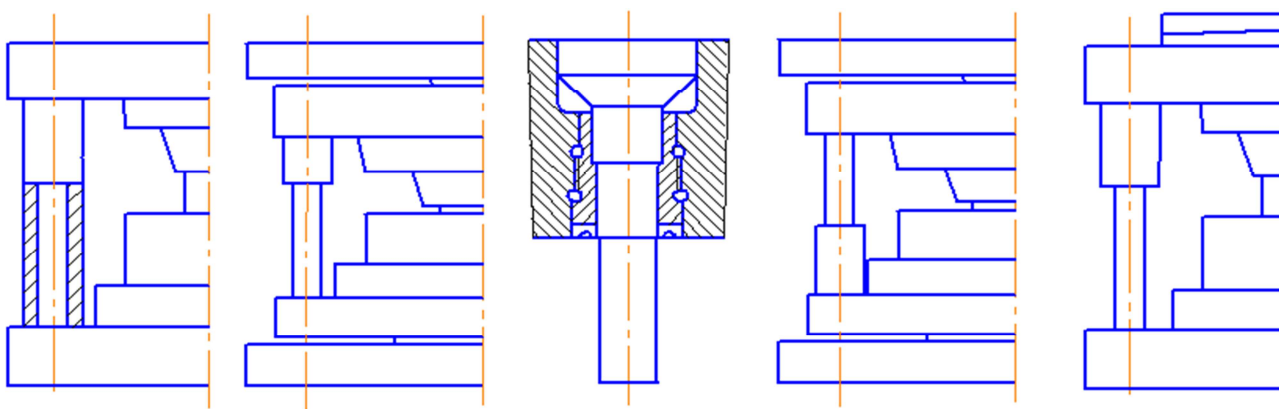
Схеми штампів, які дозволяють зменшити допусків на видавлювання
